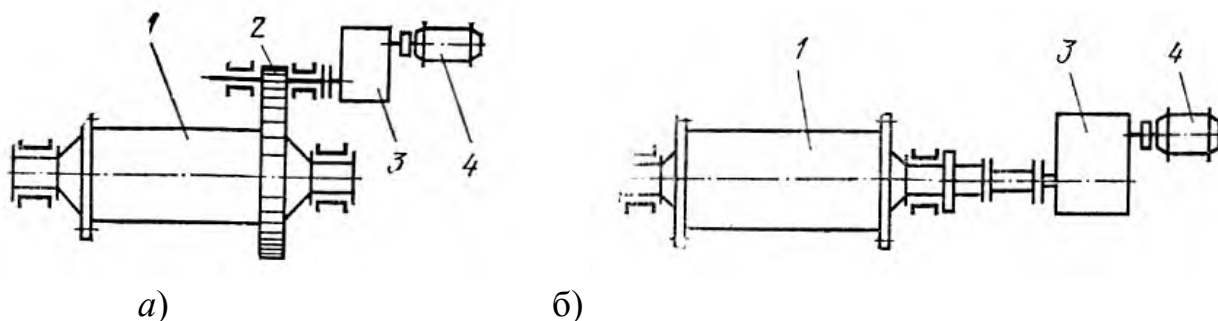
Схемы приводов вращения барабанных мельниц с боковым (а) и центральным (б) приводом: 1 – барабан, 2 – открытая зубчатая передача, 3 – редуктор, 4 – электродвигатель
